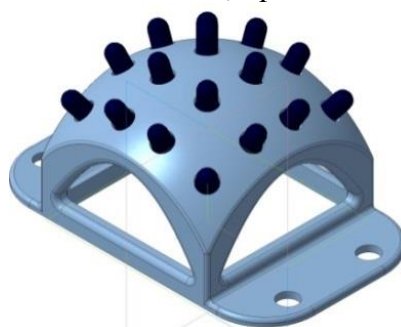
Конструкция корпуса макета разрабатываемой системы
